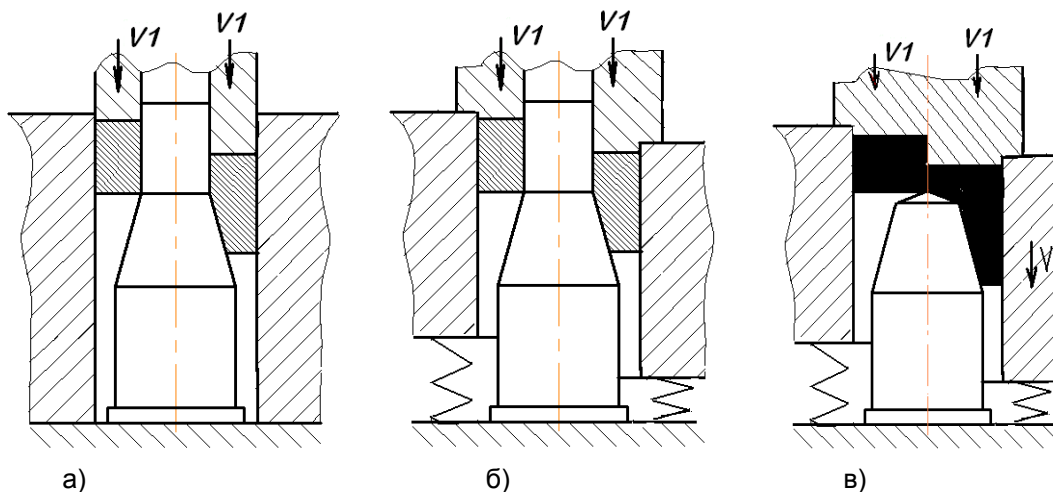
Деформирование кольцевых заготовок выдавливанием в зазор между неподвижными контрпуансоном и матрицей (а) и неподвижным контрпуансоном и подвижной матрицей (б); выдавливание сплошной заготовки в зазор между неподвижным контрпуансоном и подвижной матрицей (в)
